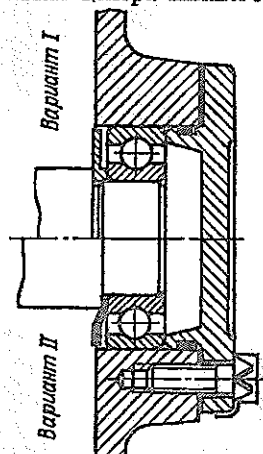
Установка защитных шайб для ограничения поступления масла в подшипник при близком расположении зубчатых зацеплений или червяка: I — точная защитная; II — штампованная защитная шайба
